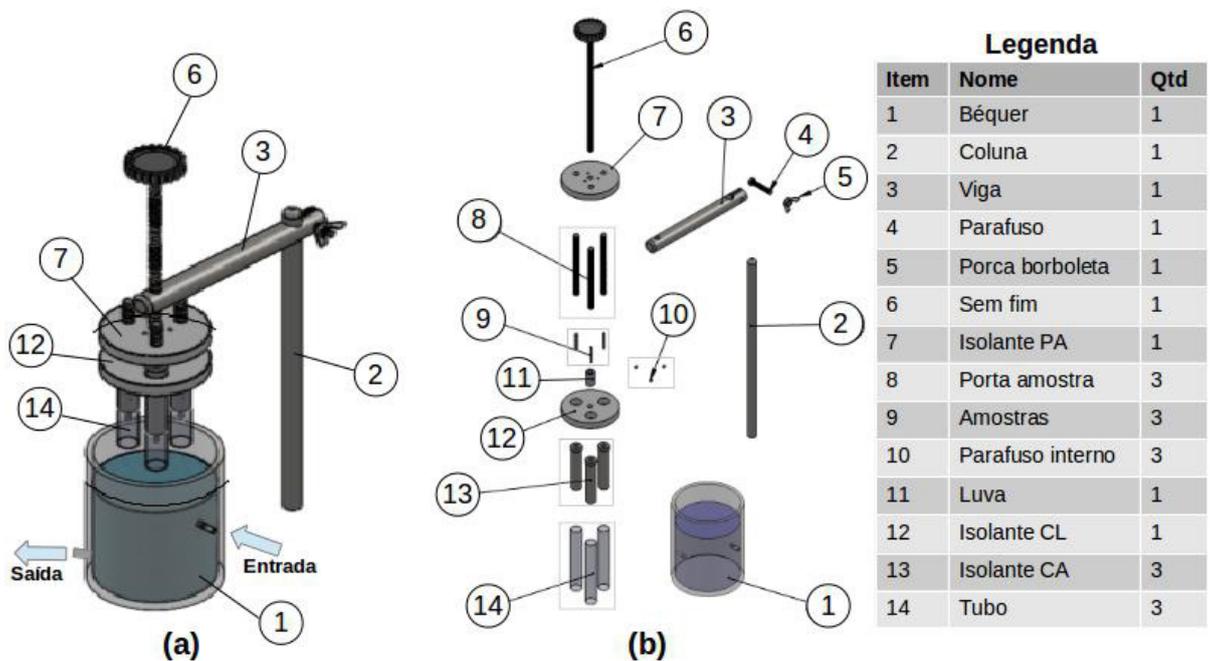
Desenho 3D do equipamento PEO (a) montado vista isométrica e (b) representação esquemática da vista explodida (Autoria própria).
